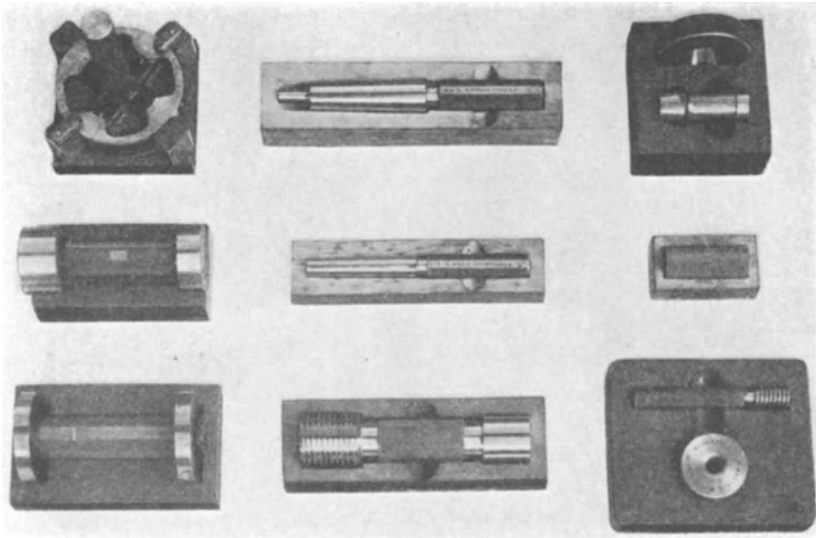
Meßwerkzeuge auf Holzbrettchen.
